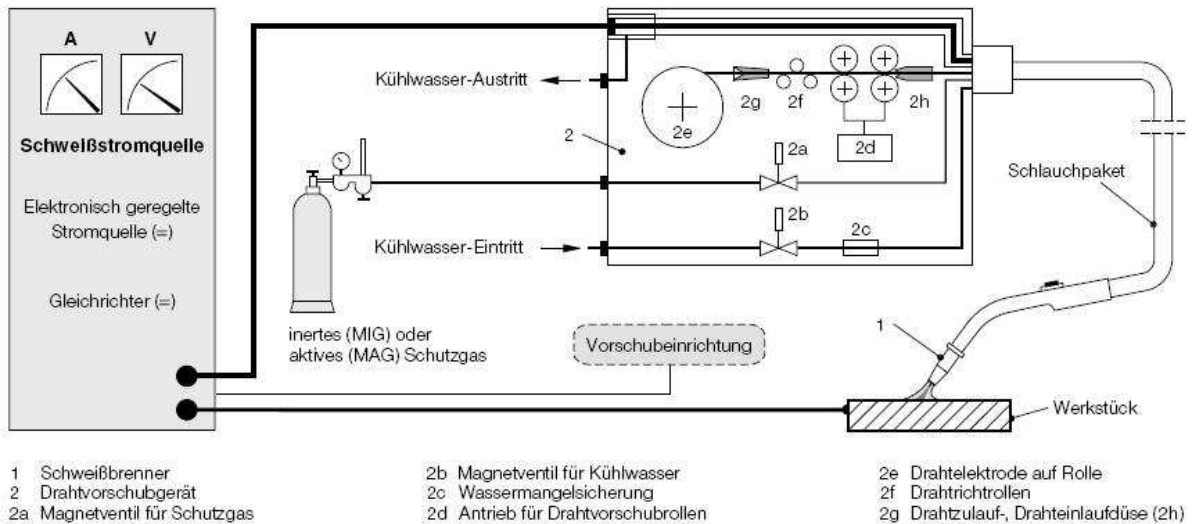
Grundsätzlicher Aufbau einer wassergekühlten MIG-Schweißanlage<sup>[ST03]</sup>
